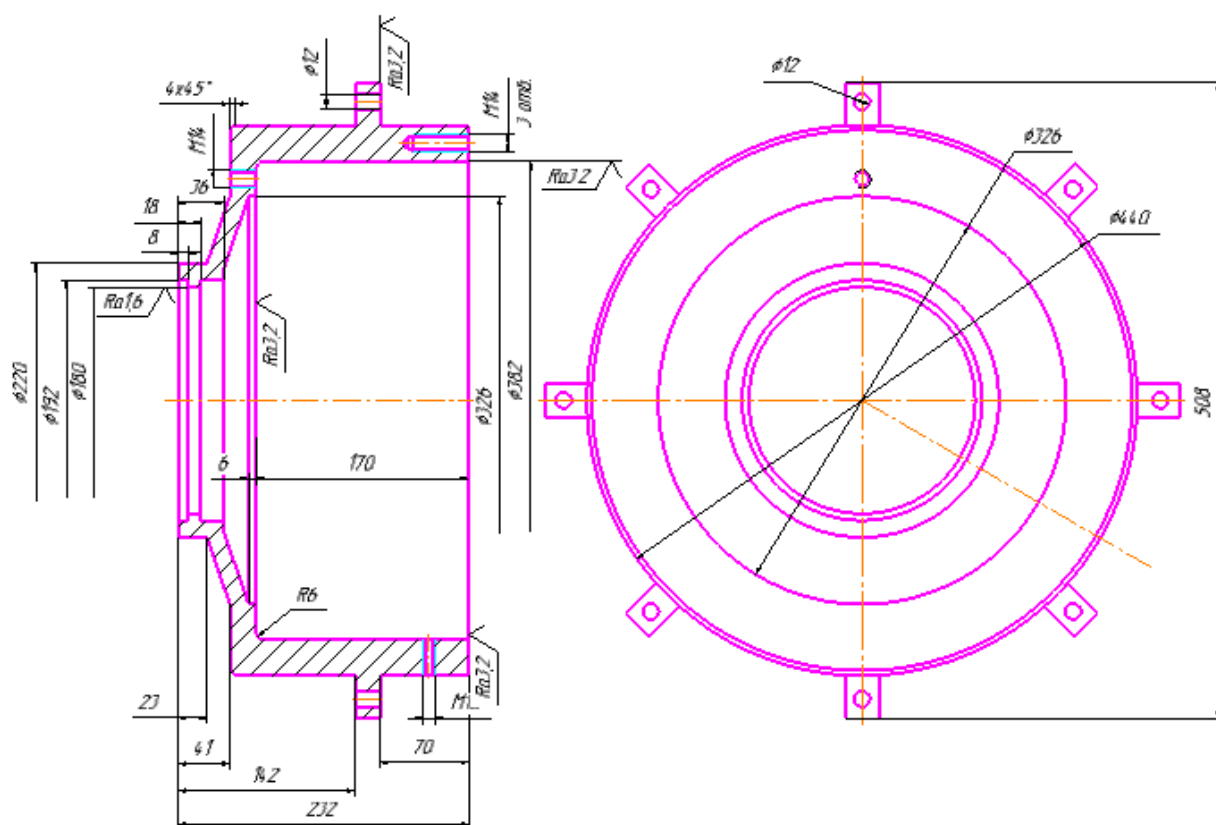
Ескізне креслення деталі "Кришка підшипника"
